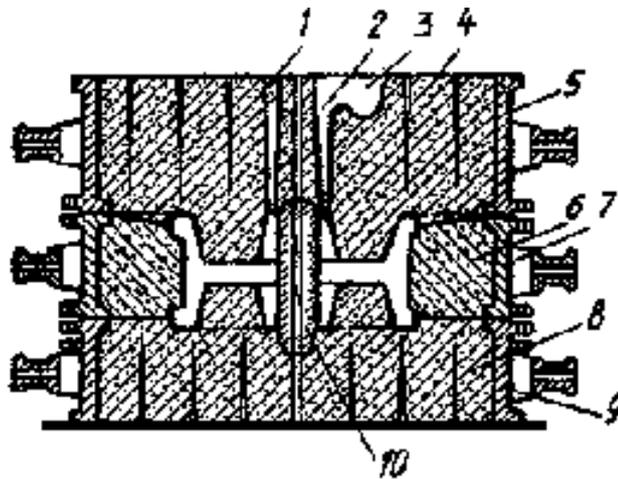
Форма для отливки шкива, изготовленная в трех опоках:
